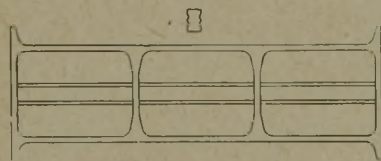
Rahmendarstellung einer Untergestellkonstruktion
